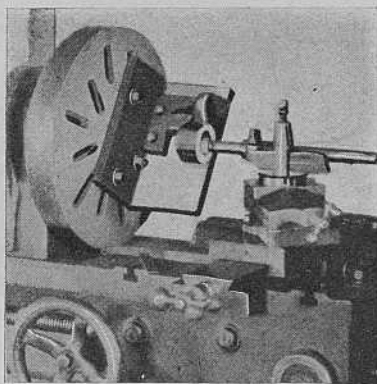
Montaje de piezas sobre una escuadra fija en el plato plano.
